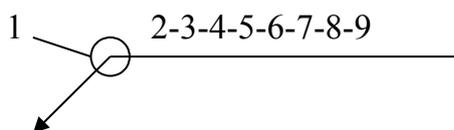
Структура условного обозначения стандартного сварного шва
